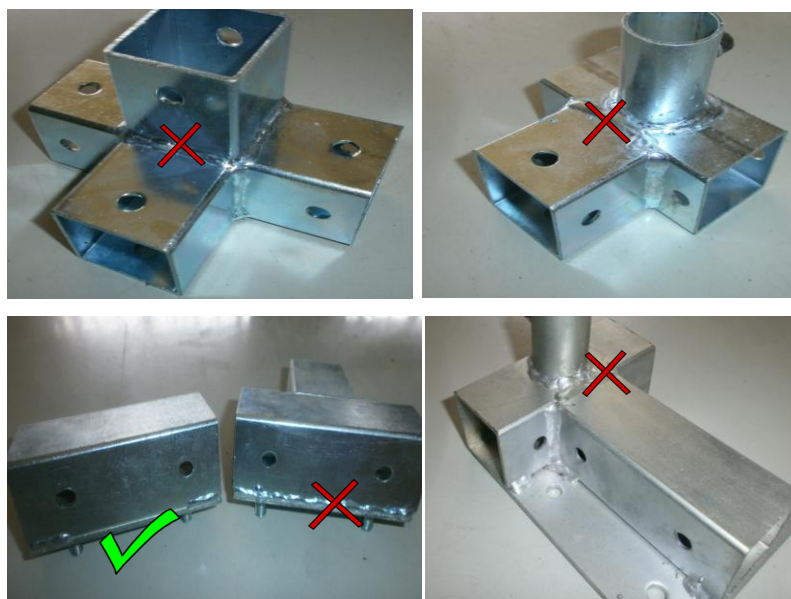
Exemplo de uma má aplicação de soldadura
